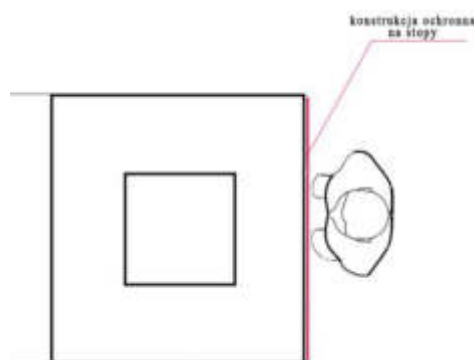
Konstrukcja ochronna przy strefach niebezpiecznych [2]
